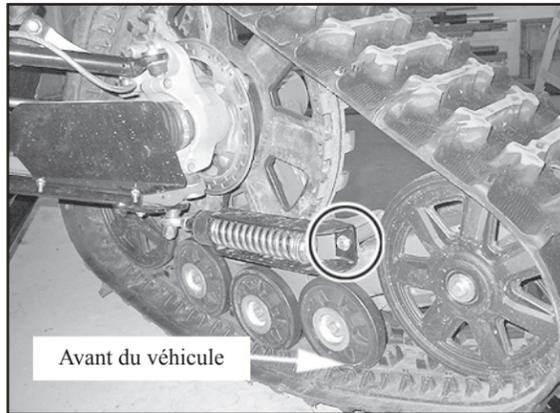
Anti-rotation avant assemblé sur l'ensemble de chenilles
